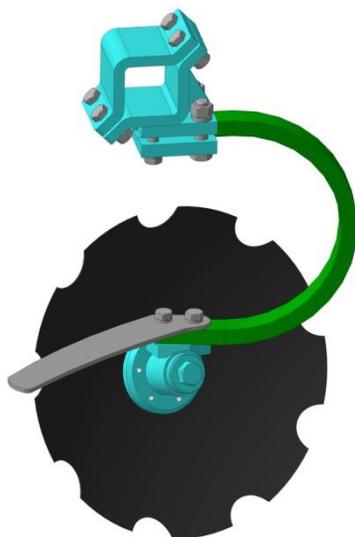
3D модель сборочной единицы «Узел режущий»
